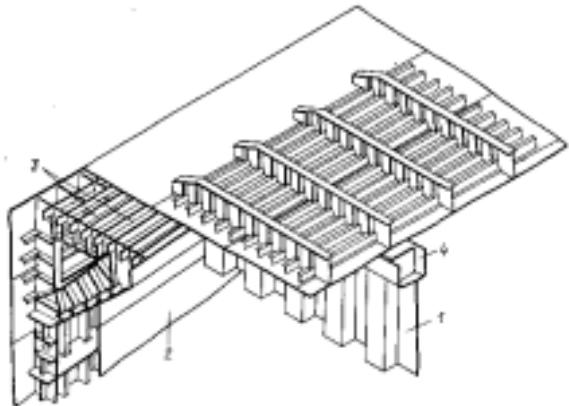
Конструкция палубы нефтеналивчика с двойными бортами:
